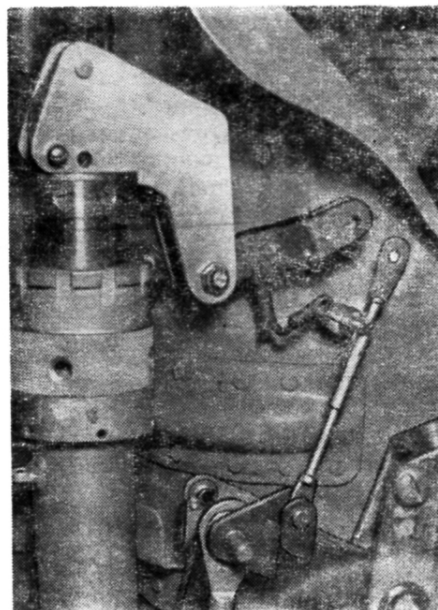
Отсоединение качалки затвора от тяги привода включения аварийного механизма притяга
